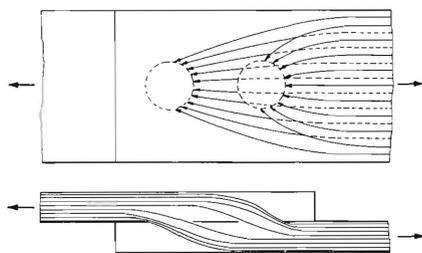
Kraftfluß in einer Punktschweißverbindung.
